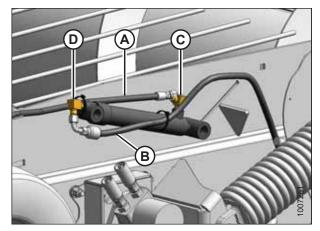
Vérin principal — Côté gauche de la plateforme
